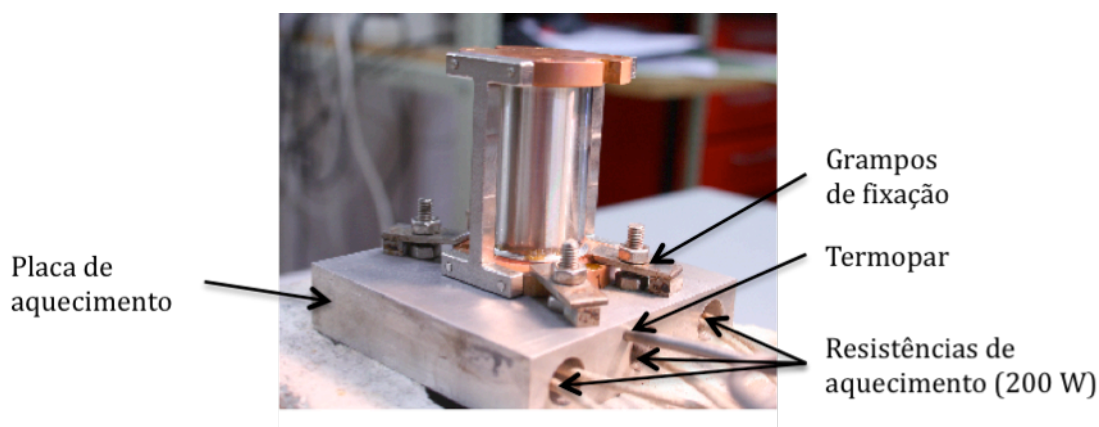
Placa de aquecimento utilizada na soldadura do dispositivo. São visíveis os 3 orifícios para as resistências de aquecimento na base de alumínio da placa. O pequeno orifício é para a colocação do termopar.
